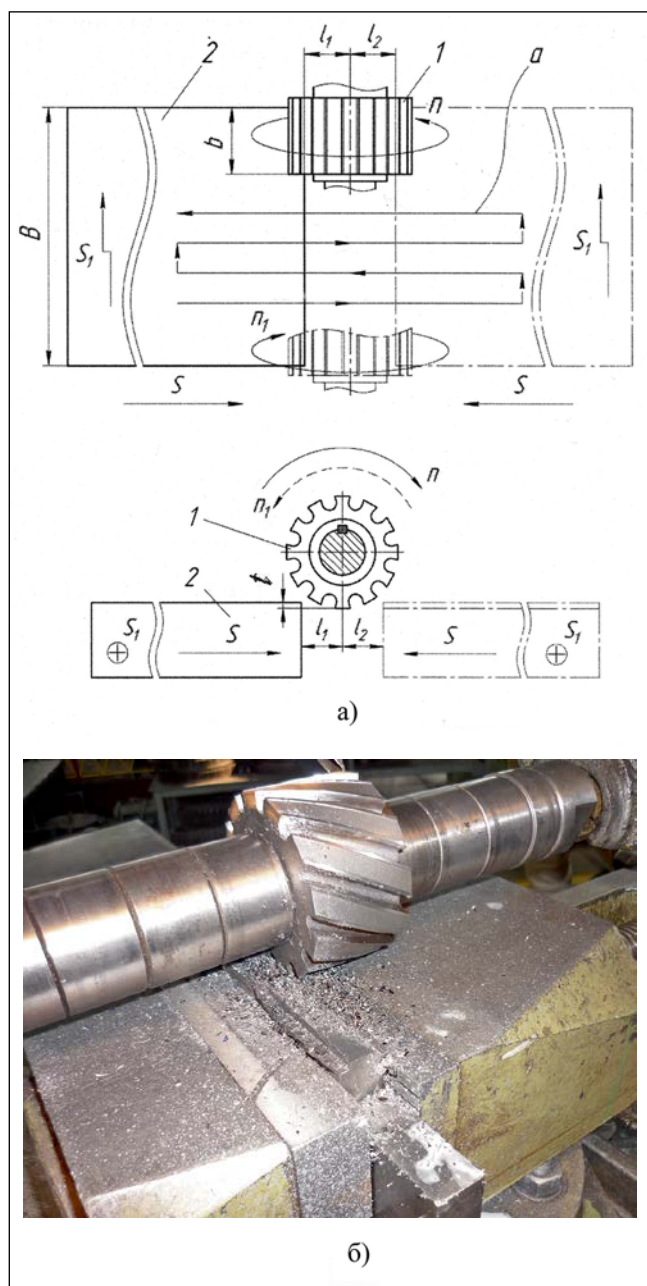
Реверсивное фрезерование: а) схема, б) реверсивная фреза. t — припуск, b — ширина резания, s — подача, a — траектории ходов стола
